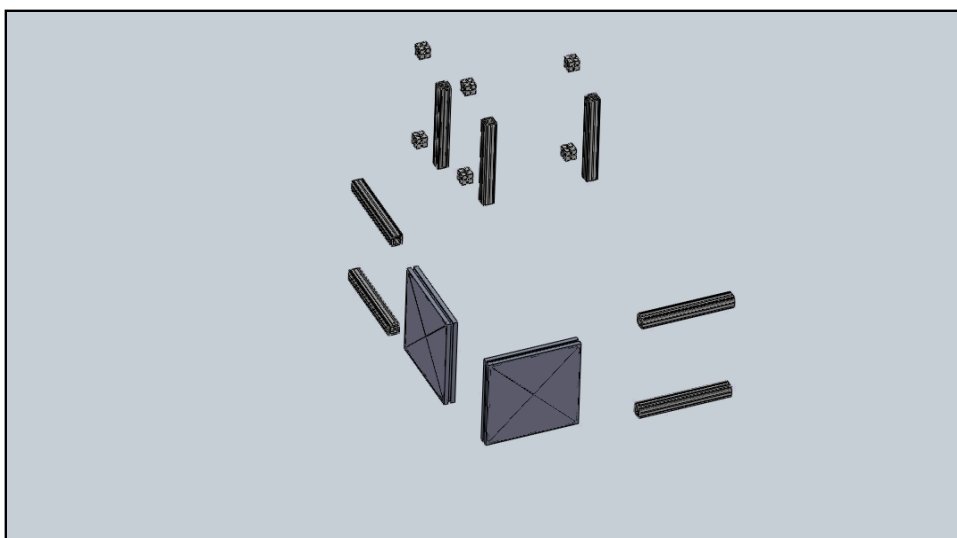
Exemplo de montagem entre conectores, ligações e chapas estruturadas.
